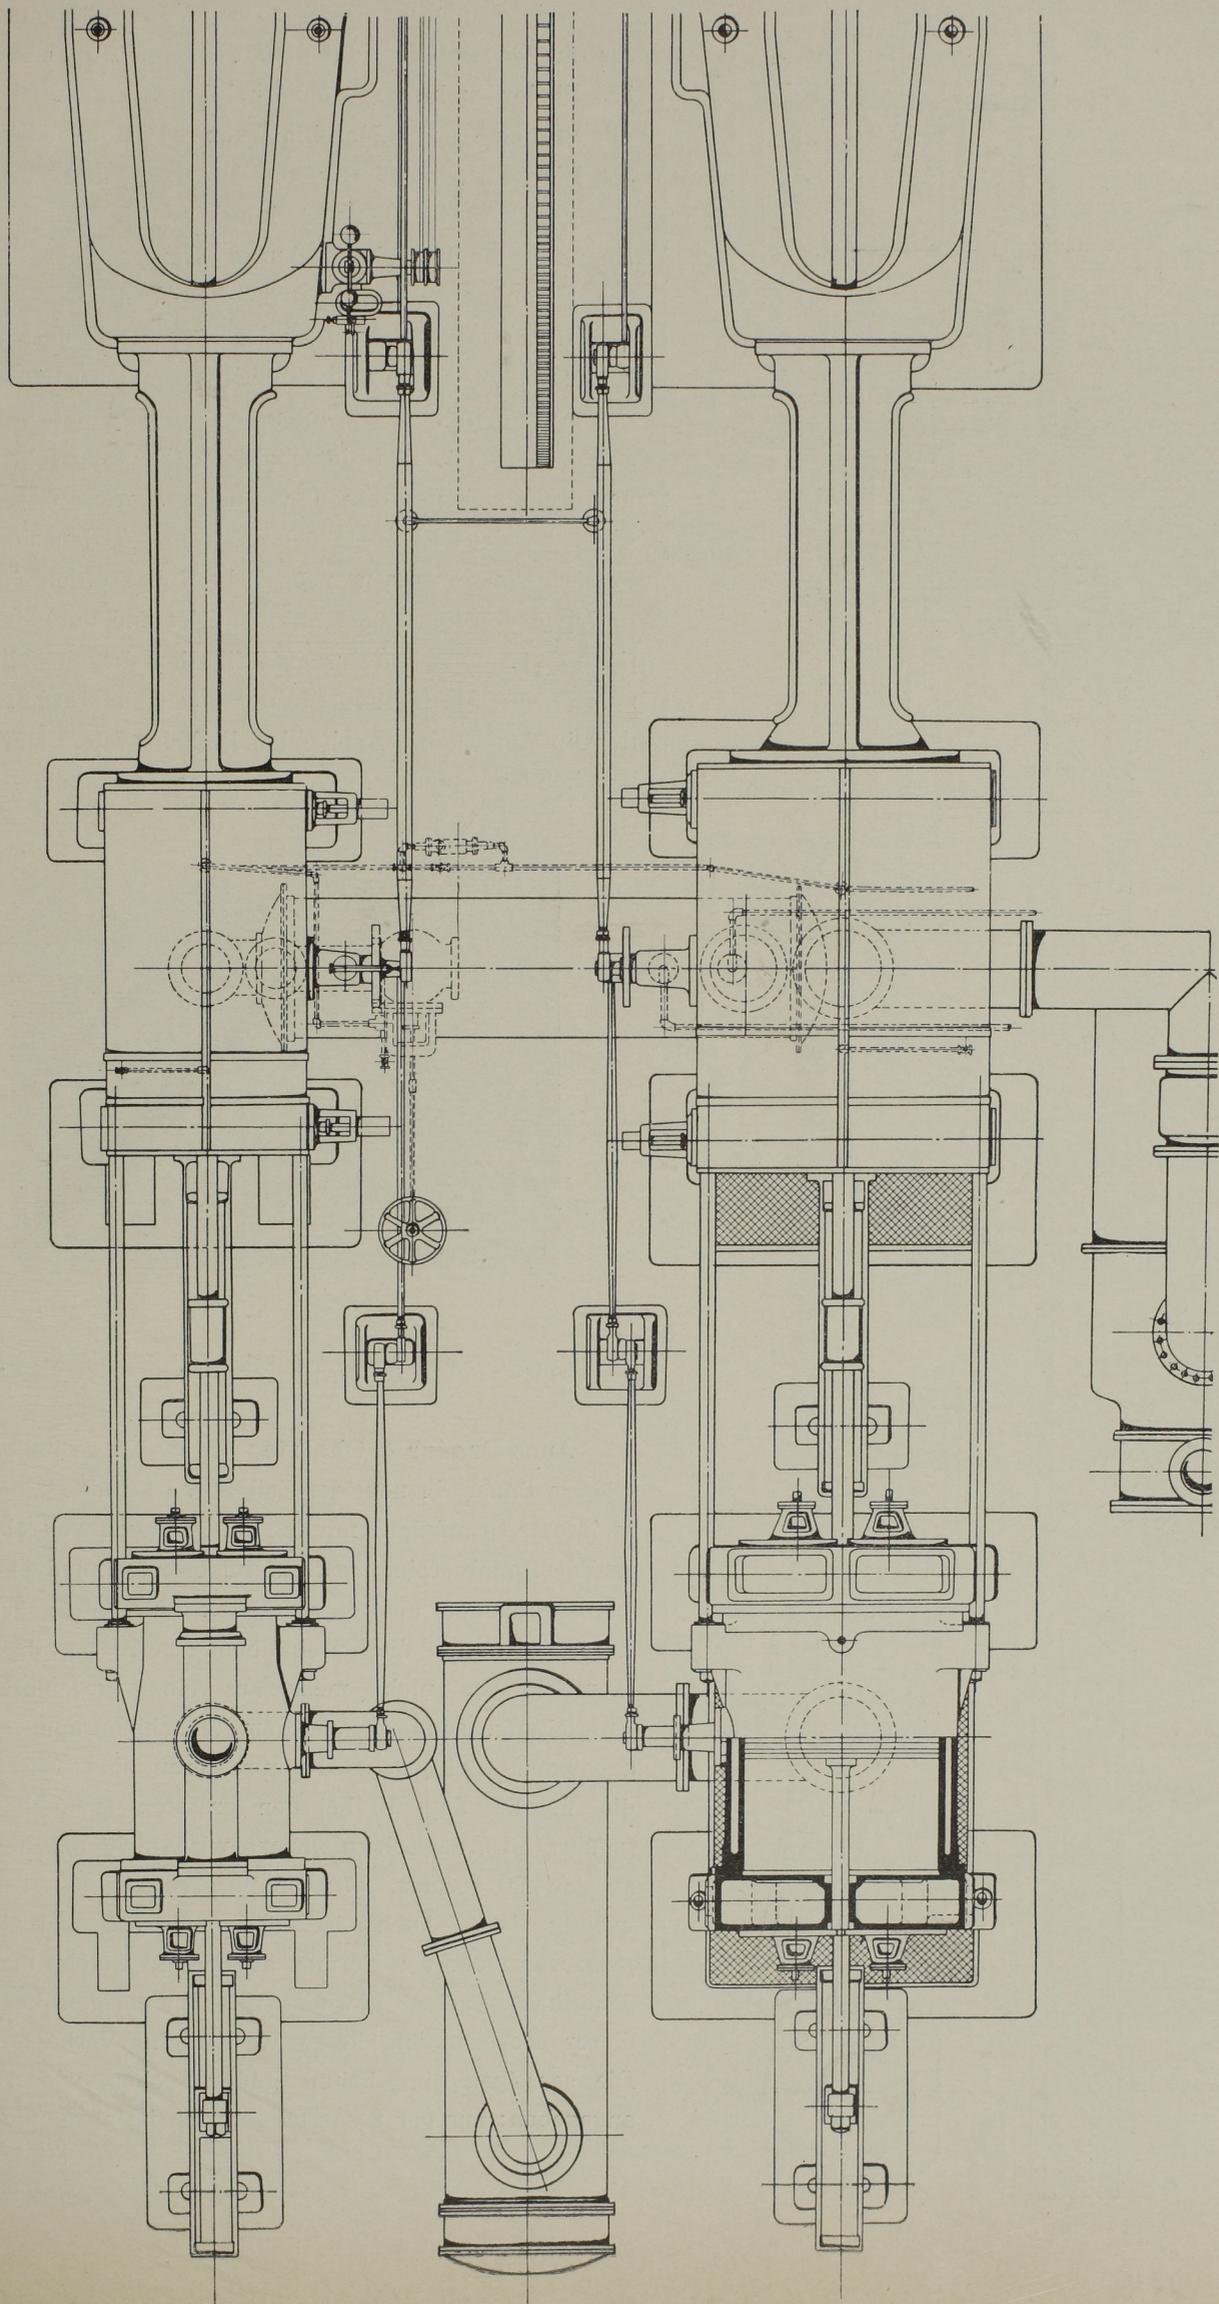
Grundriss der Maschine. Massst. 1 : 48.
